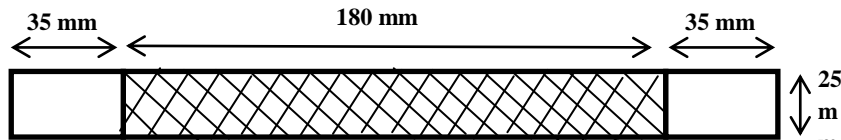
Géométrie d'éprouvette de traction découpée à partir d'un tube en PRV.
